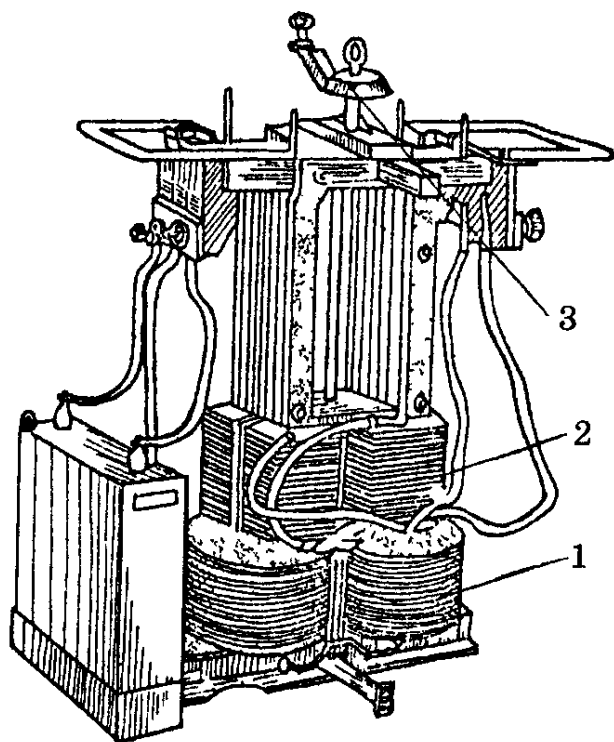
Сварочный трансформатор типа ТСК-500
